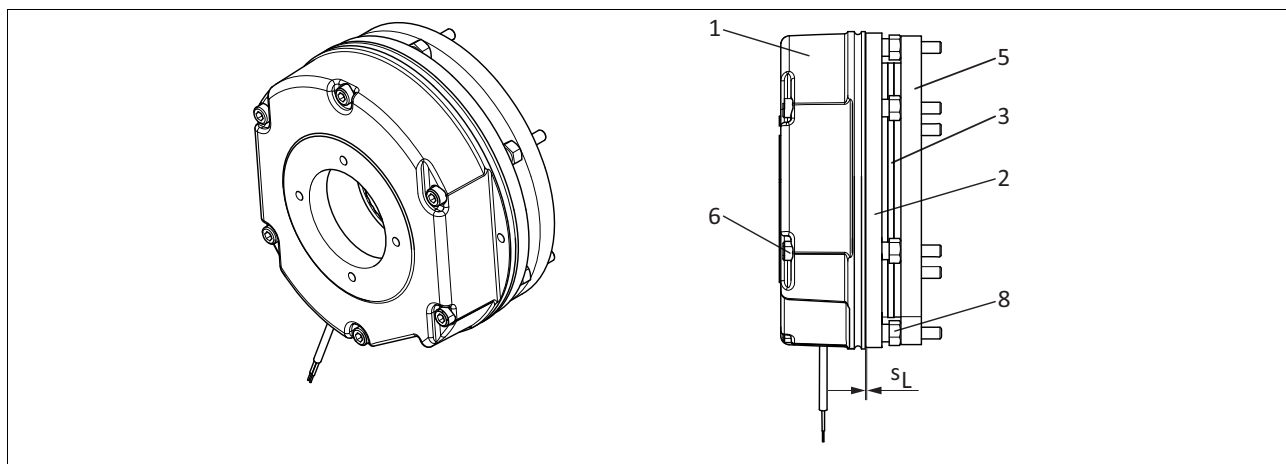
Aufbau einer Federkraftbremse INTORQ BFK458: Grundmodul E (Magnetteil komplett) + Rotor + Nabe + Flansch
